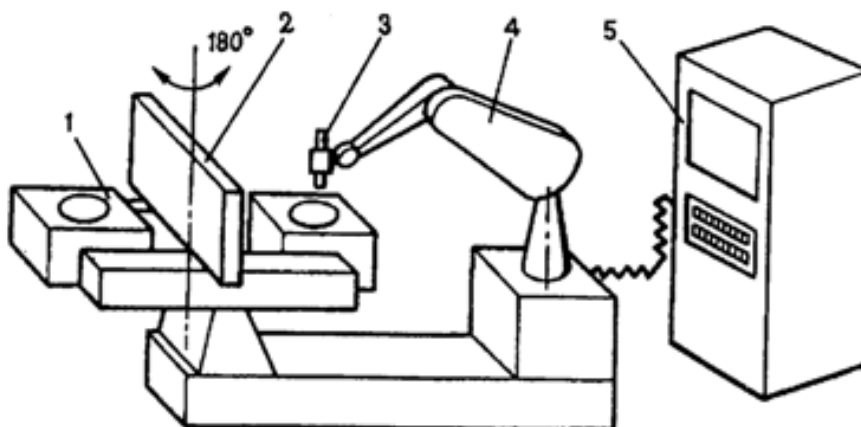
Схема робототехнического комплекса для сварки корпусных деталей
